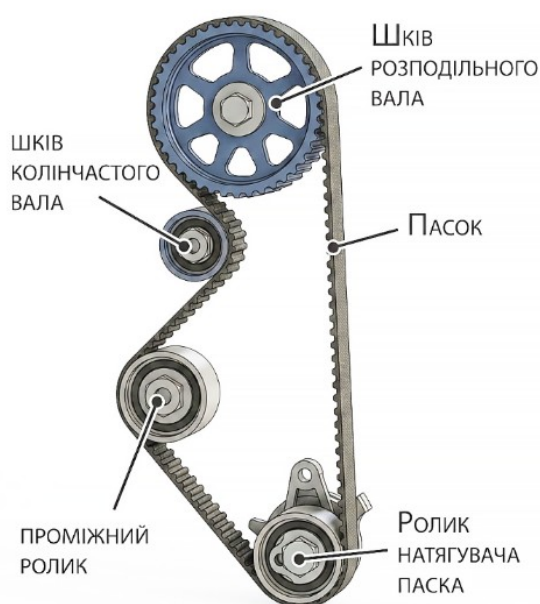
Схема паскового приводу газорозподільного механізму.
